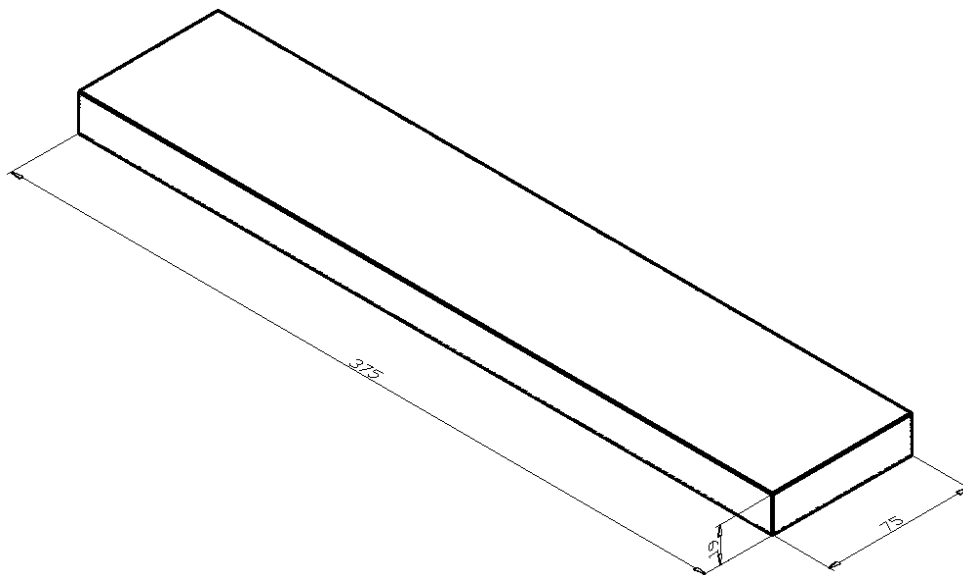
1. Cupón para soldadura de recargue (dimensiones en mm).
